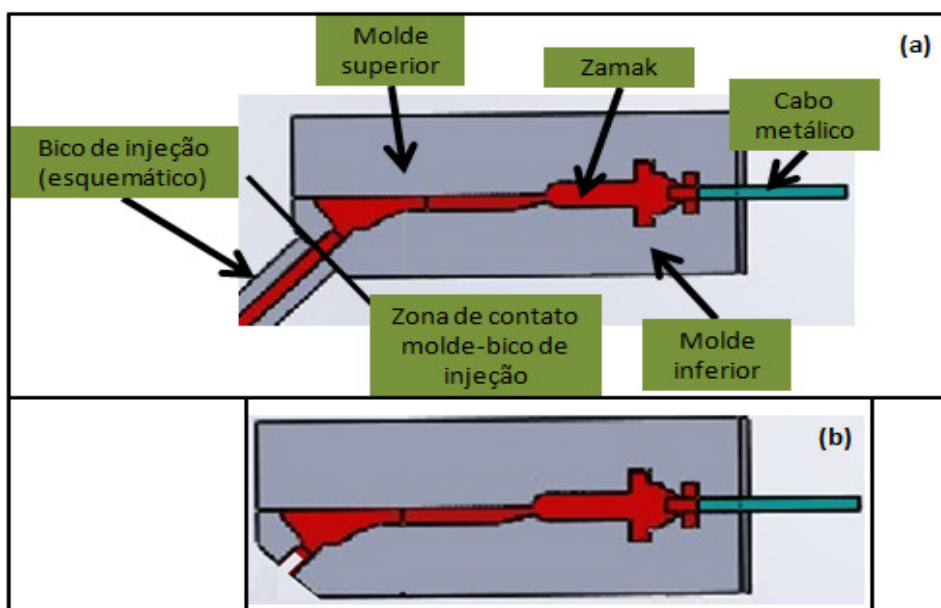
Esquema de injeção; (a) Acoplamento bico/molde; (b) Molde após injeção.
